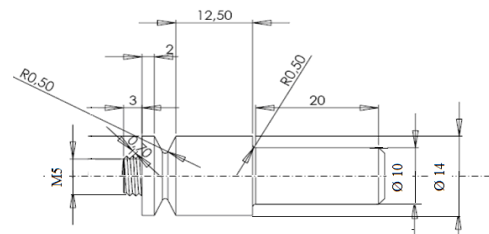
Outil de soudage par point par friction malaxage
